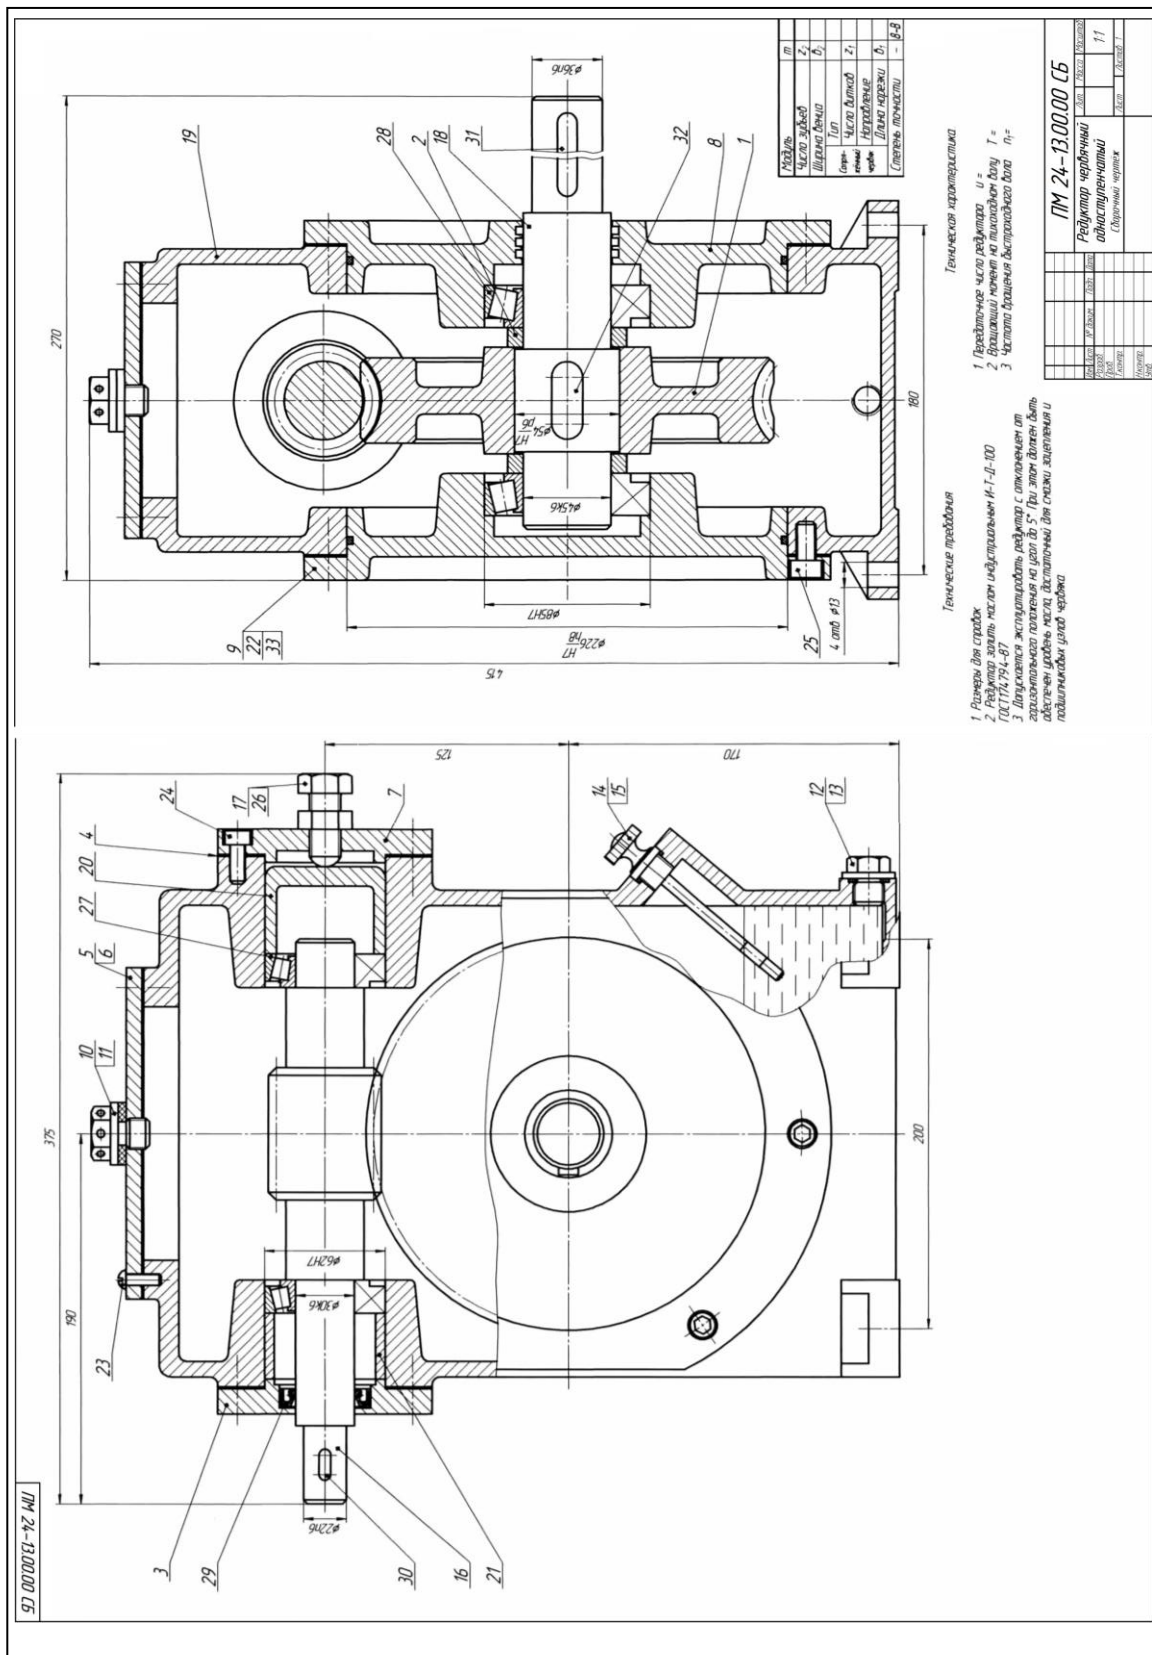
Пример сборочного чертежа одноступенчатого червячного редуктора с верхним расположением червяка
